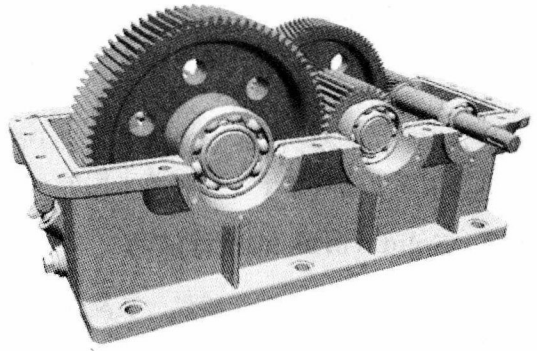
二级圆柱齿轮减速器齿轮及底座
